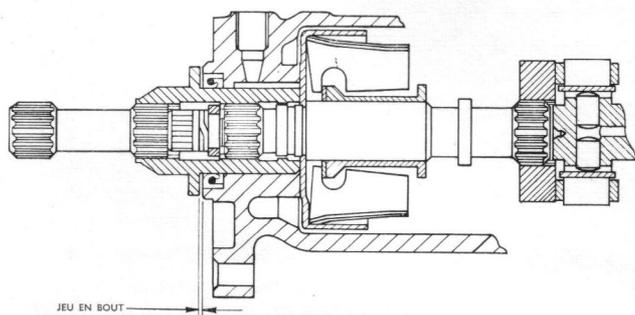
Vue de l'entraînement à fourreau illustrant le jeu en bout
